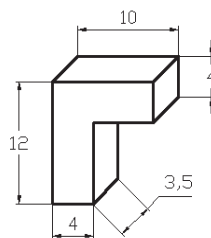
Geometría final del concentrador maquinado (unidades: mm).
